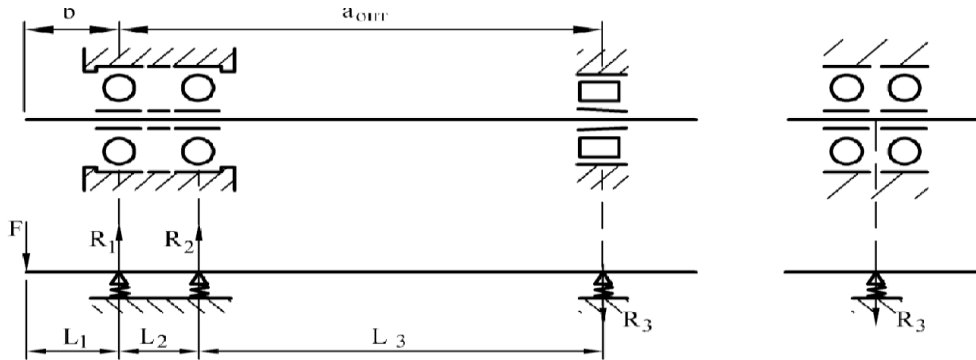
Розрахункова і конструктивна схеми шпиндельного вузла з двома підшипниками в передній опорі
